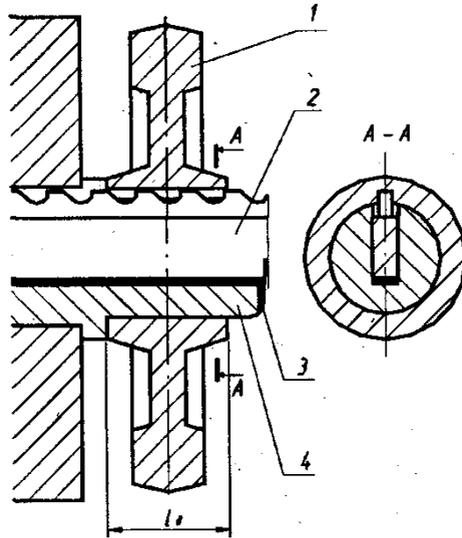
Пример протягивания шпоночного паза в основном отверстии зубчатого колеса:
